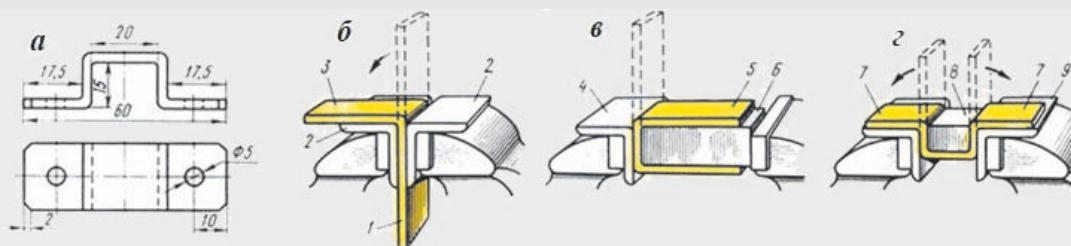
Виготовлення скоби зі смугової сталі: а — готова деталь; б — загин першої опори; в — загин другої опори; г — згинання скоби
